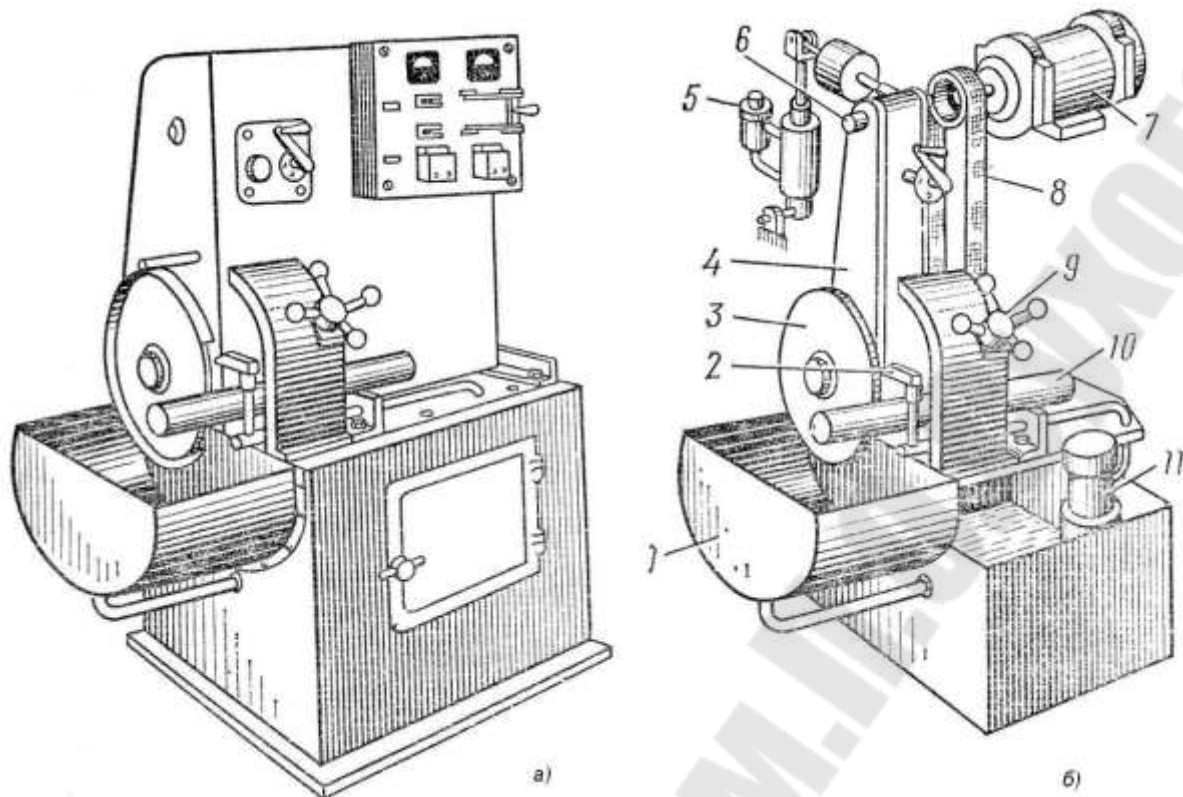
Общий вид (а) и схема анодно-механического станка
